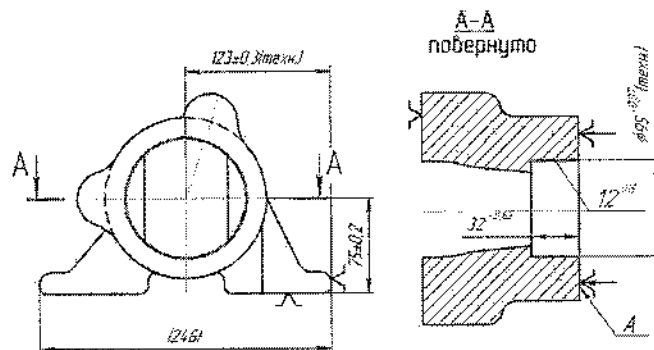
Эскиз заготовки, поступающей на операцию
